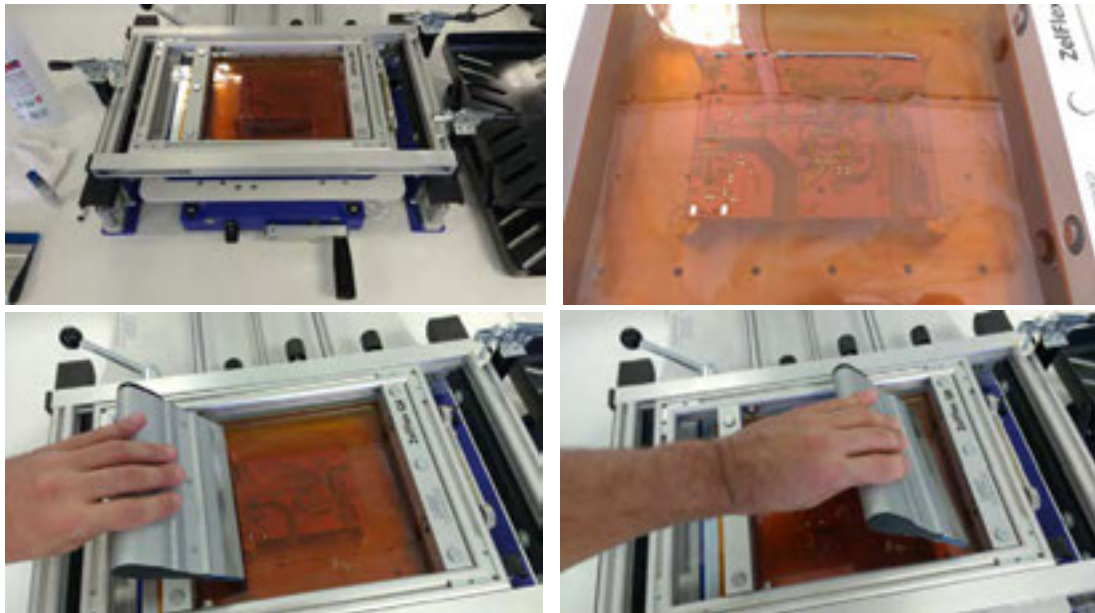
Proceso de montaje de componentes, colocación de pasta de soldadura con stencil realizado en el Plotter Fresador a partir del diseño de las máscaras con KICAD.
